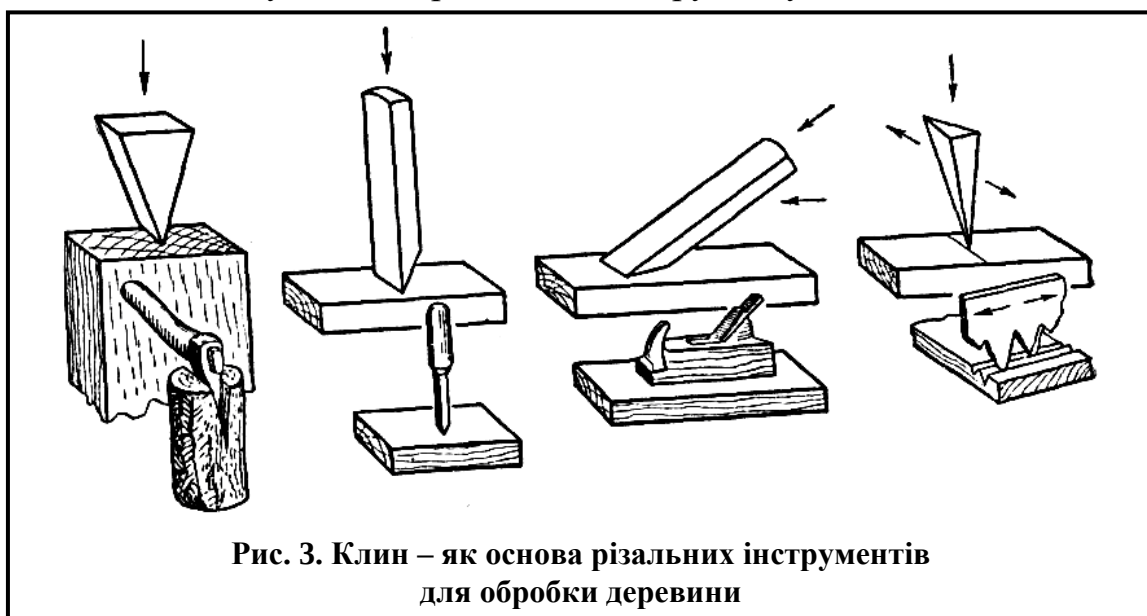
Клин – як основа різальних інструментів для обробки деревини
